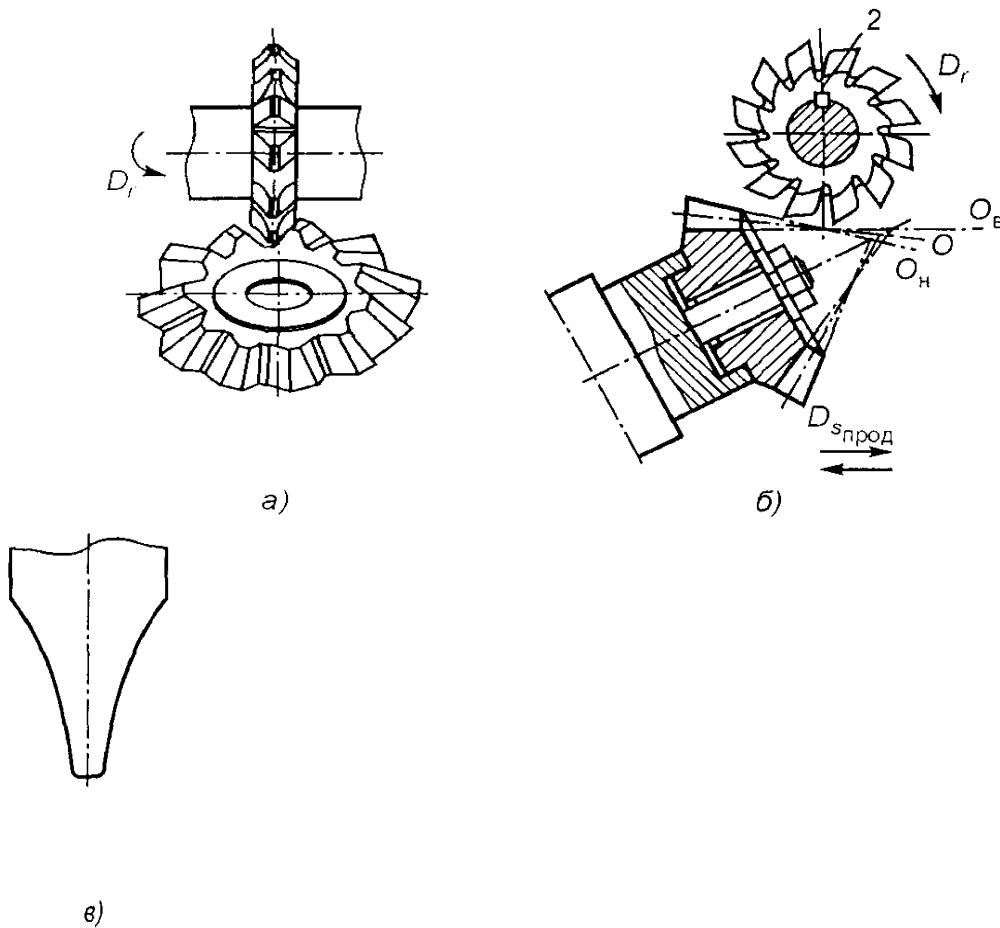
Схема нарезания прямозубого конического колеса дисковой модульной фрезой за один проход
